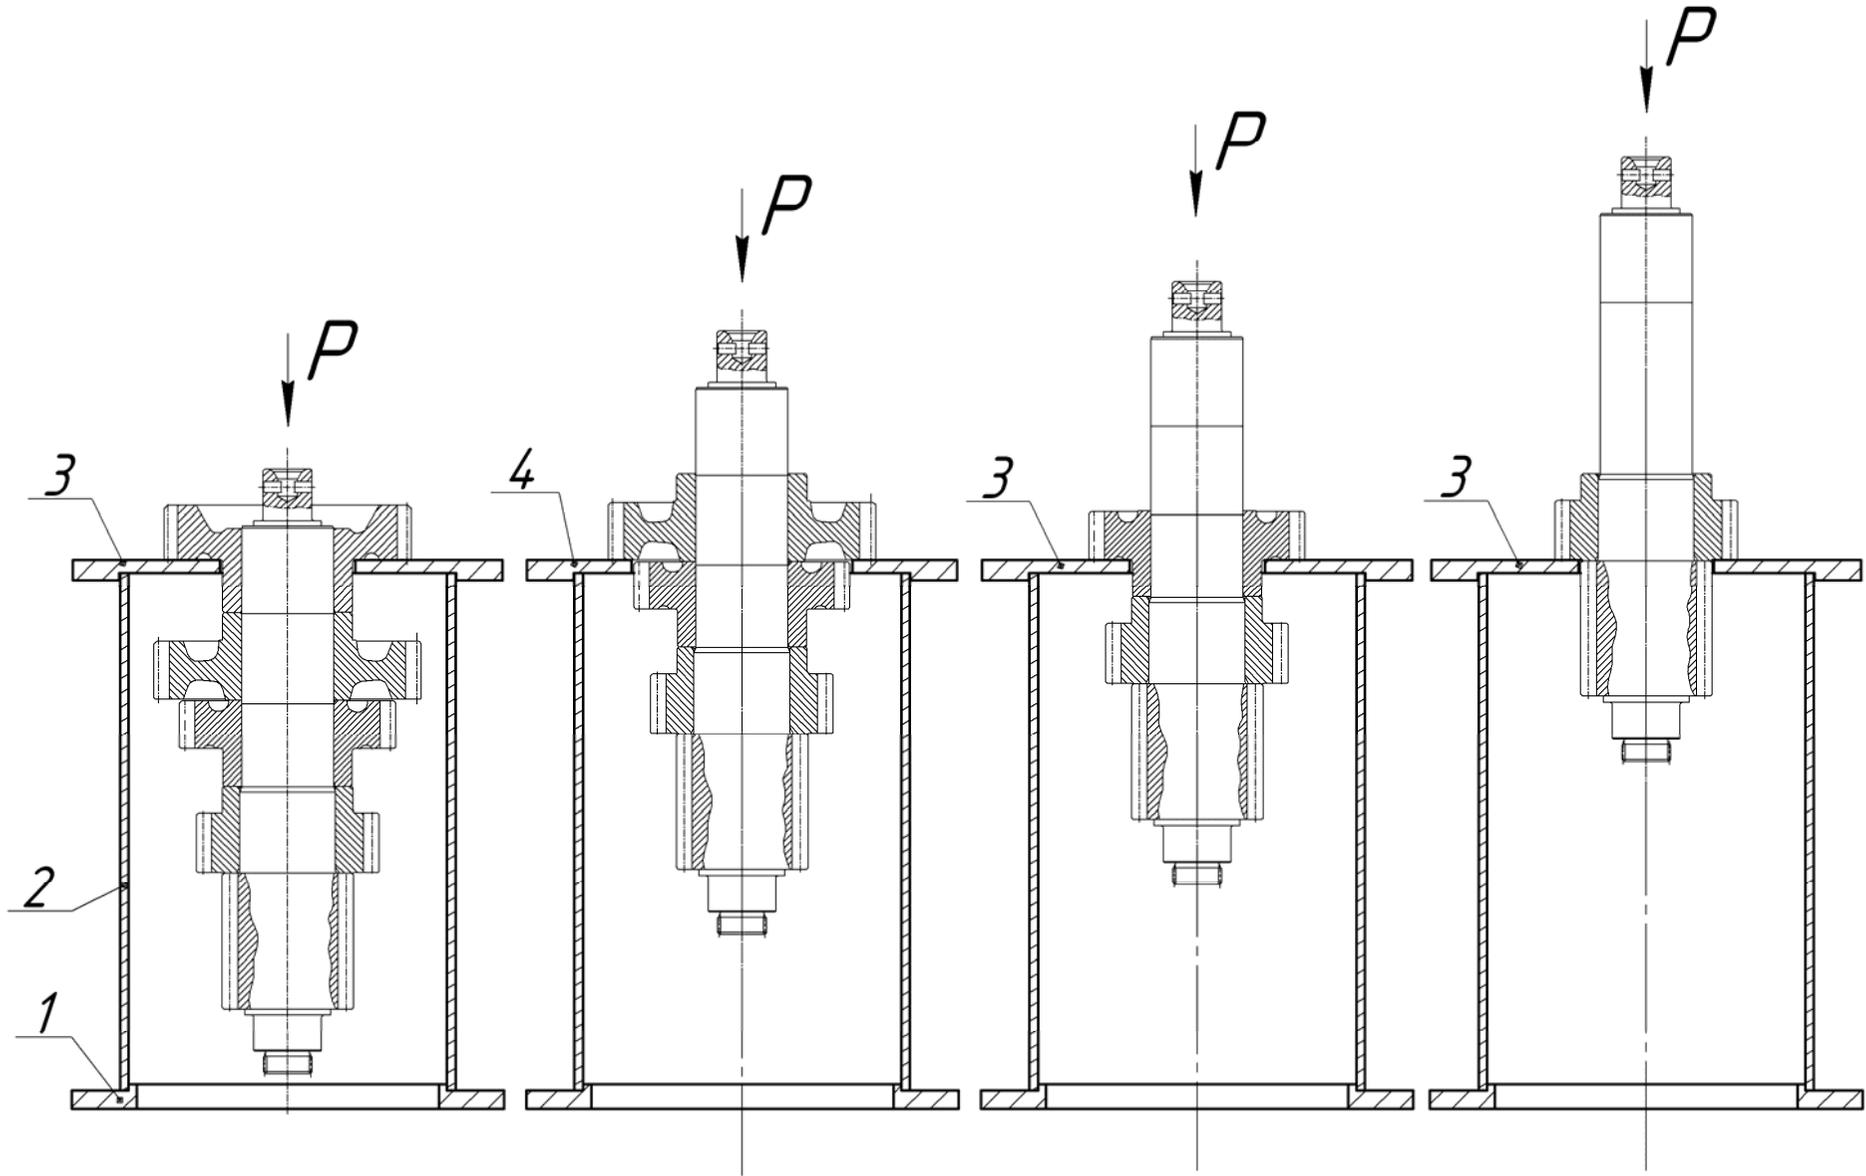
Определение размера кольца пружинного упорного 5, 10 , 28 вала вторичного
